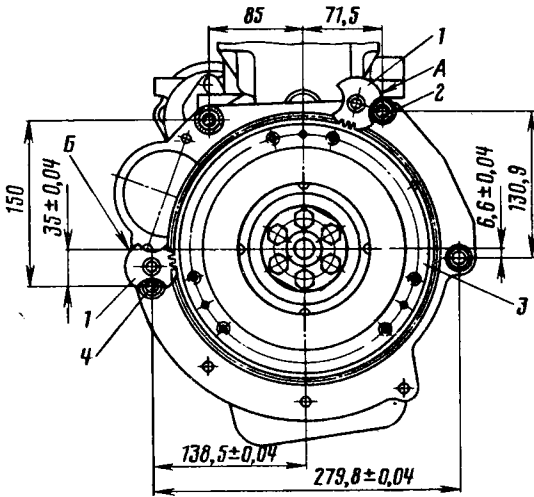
Стопорение маховика при разборке и сборке: 1 — зубчатый стопор маховика; 2 — втулка приспособления для крепления двигателя при разборке и сборке; 3 — маховик; 4 — болт; А — стопорение маховика при установке двигателя на приспособление; Б — стопорение маховика (двигатель на приспособление не установлен)
